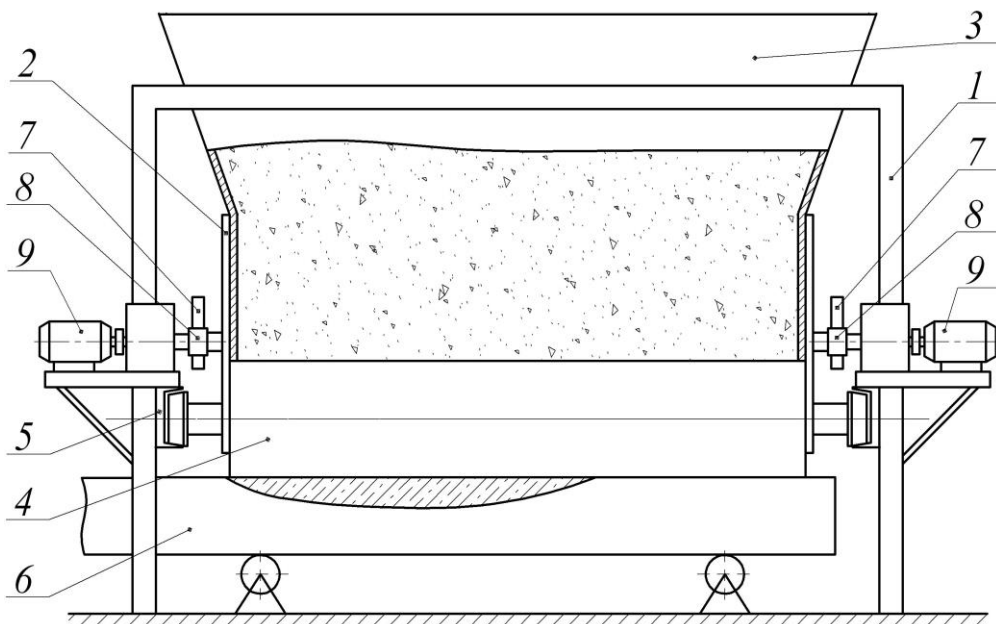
Роликова формувальна установка з кулачковим приводним механізмом
